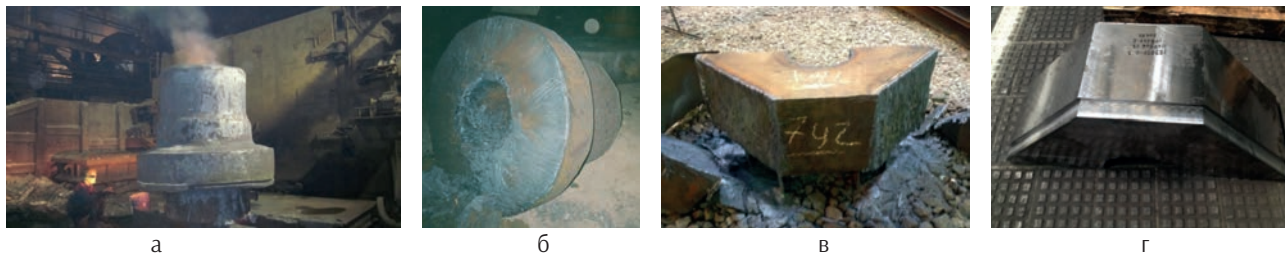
Газокислородная обрезка заготовок для уменьшения объема механической обработки: а – стальной поковки заготовки вала – шестерни мощной дробилки (сталь 38ХГН); а – рабочий момент; б – внешний вид обрезанной поковки; в - толстостенная заготовка (поковка) после газокислородной резки (сталь 35Л); г – эта же деталь после механической обработки
